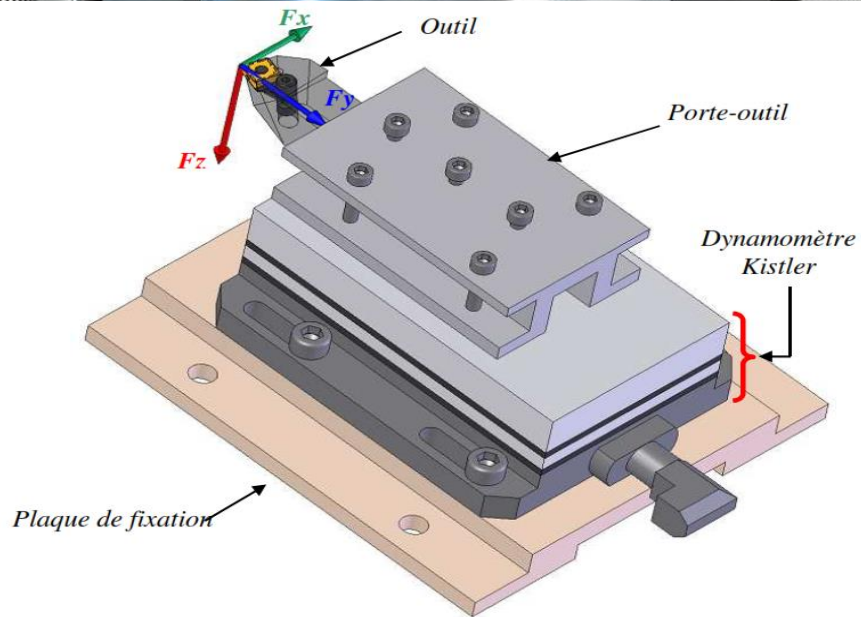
Montage du dynamomètre sur la table de la machine.
